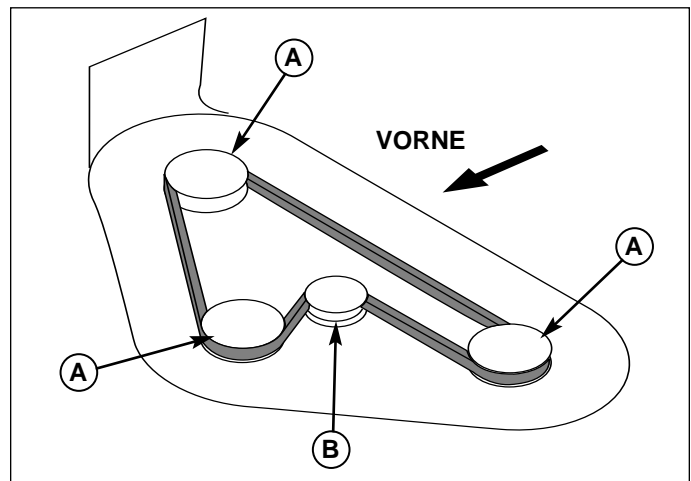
Riemenführung Mähwerk - Alle Modelle
